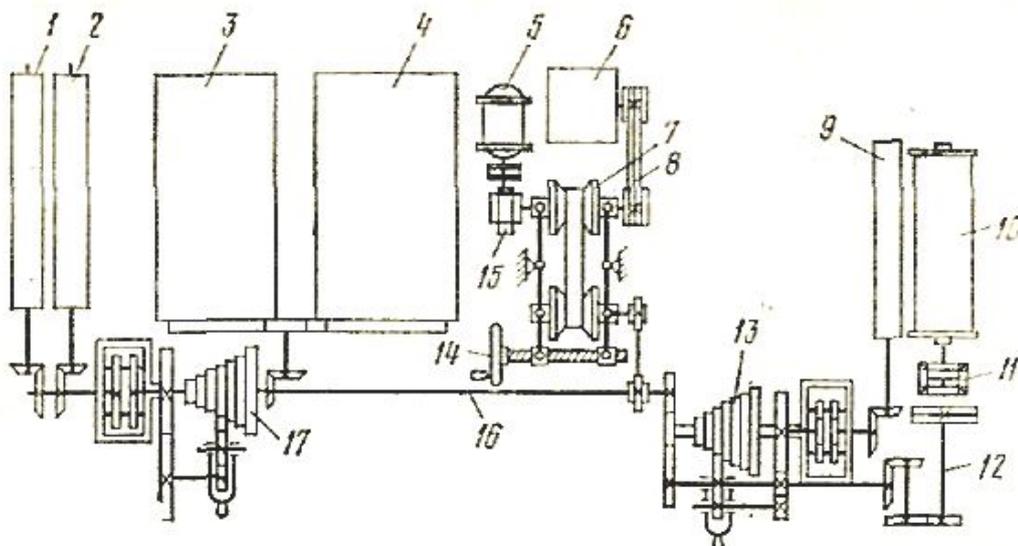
Схема шлифовальной барабанной машины: 1- тянущий вал, 2- отжимной вал, 3- малый сушильный барабан, 4- большой сушильный барабан, 5- электродвигатель тихого хода, 6- электродвигатель рабочего хода, 7- вариатор, 8- клиноременная передача, 9- выпускной вал, 10- ткацкий навой, 11- дифференциальный фрикцион, 12- валик, 13- передний уравнильный механизм, 14- винт вариатора, 15- червячная передача, 16- мажорный вал, 17- задний уравнильный механизм.
